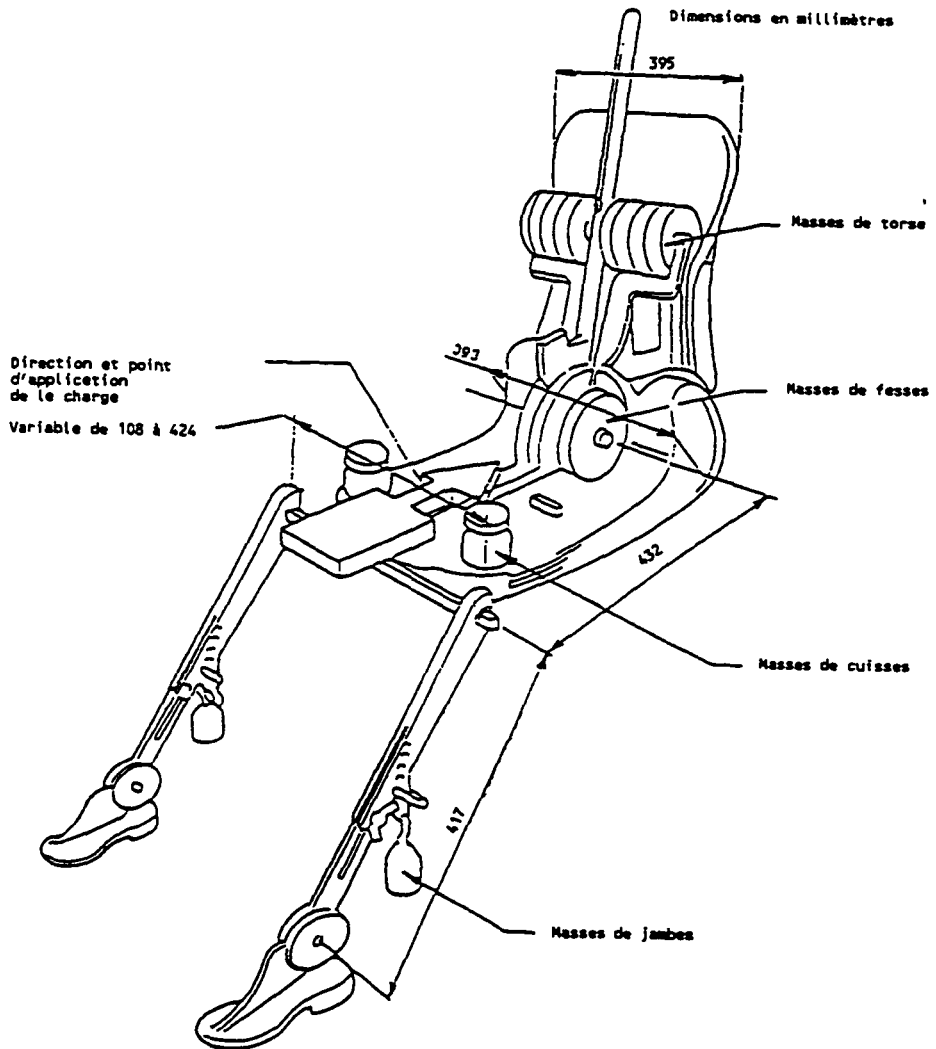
Dimensions des éléments de la machine 3-D H et emplacement des masses
